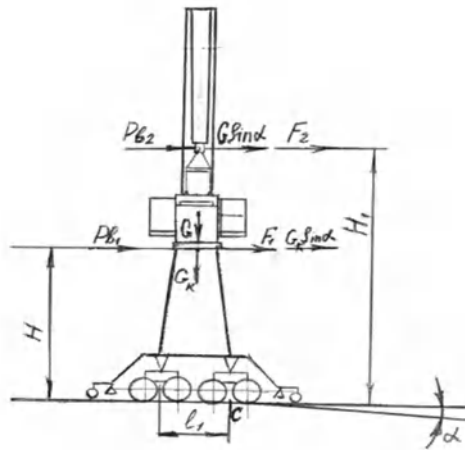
Розрахункова схема вантажної стійкості крана при пересуванні з вантажем
